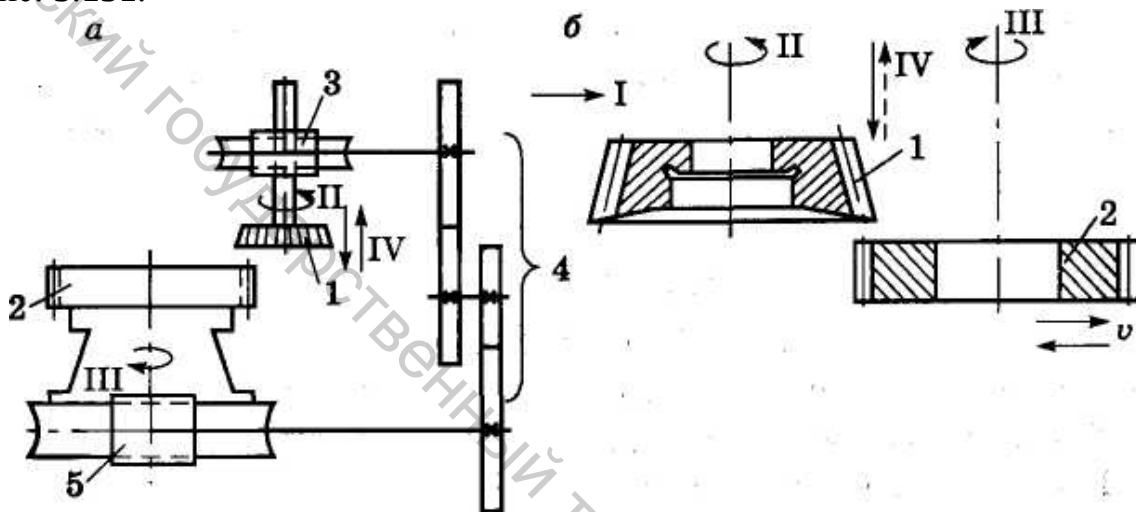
Схема зубодолбежного станка (а) и направления основных движений при нарезании зубьев прямозубого колеса долбяками (б): 1— долбяк; 2— нарезаемое колесо; 3— делительная червячная пара шпинделя долбяка; 4— сменные колеса; 5— делительная червячная пара стола
